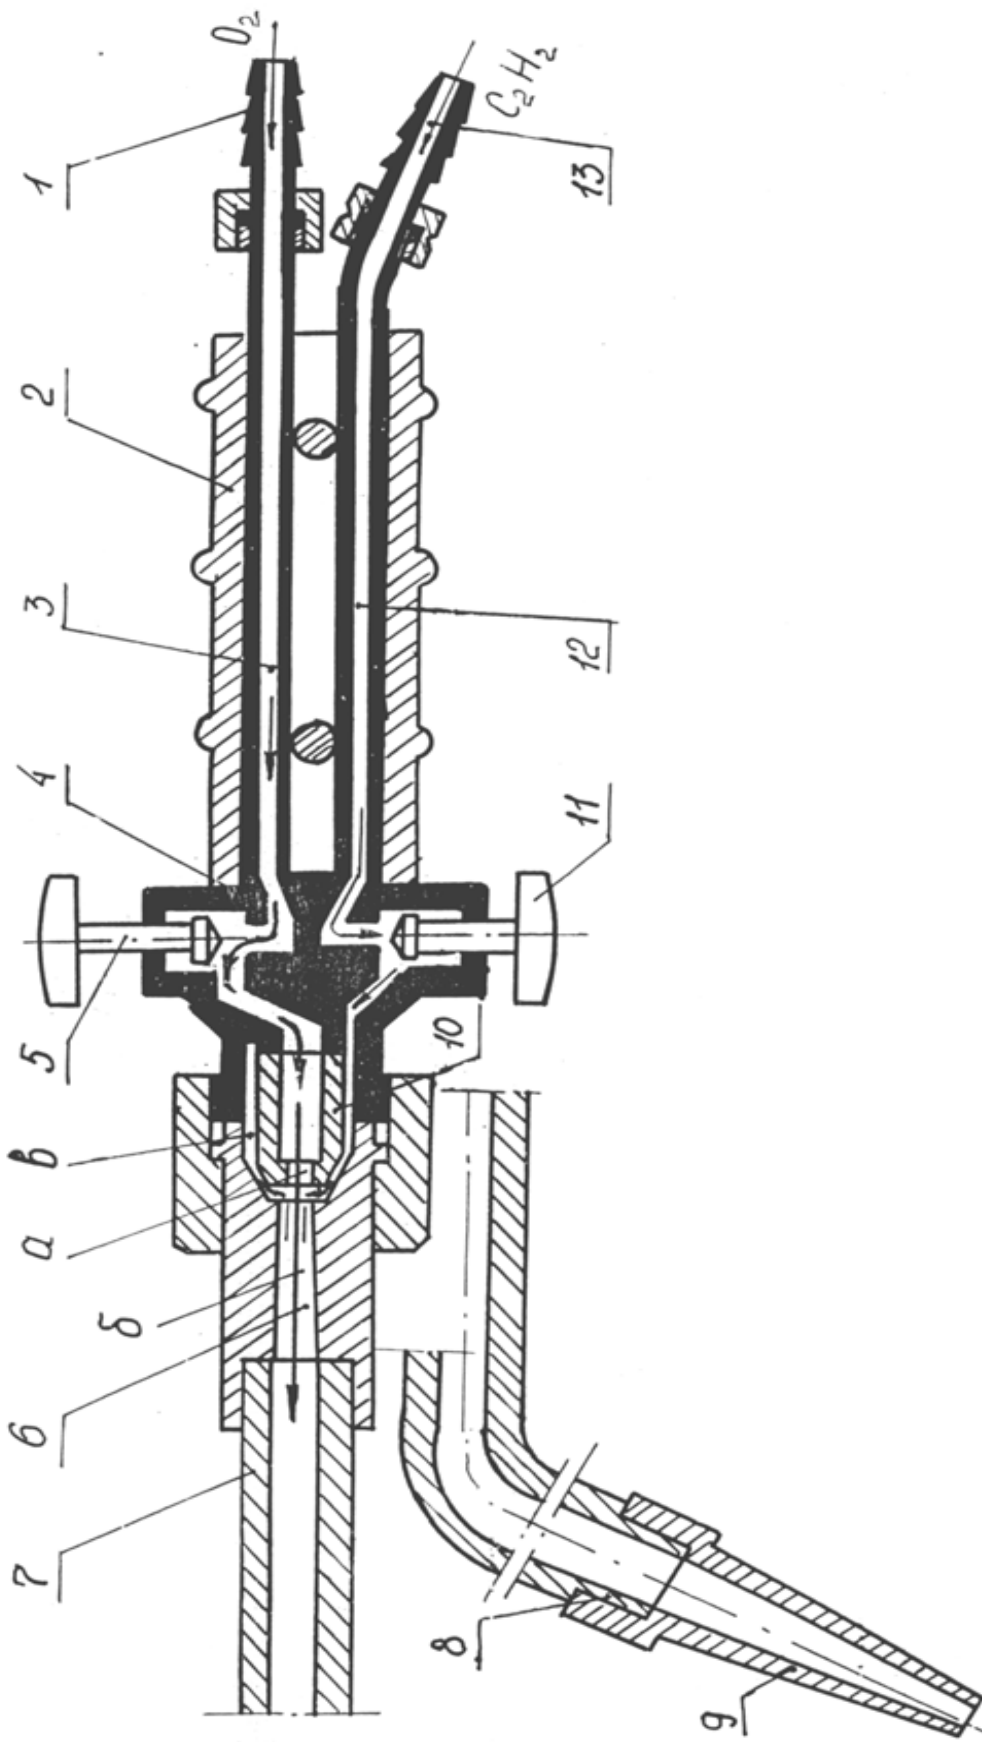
Схема инжекторной горелки. 1 - кислородный нипель; 2 - рукоятка горелки; 3 - трубка для транспортирования кислорода; 4 - корпус; 5 - вентиль кислорода; 6 - смешительная камера; 7 - трубка для подачи горючей смеси; 8 - штуцер; 9 - мундштук; 10 - инжектор; 11 - вентиль ацетилена; 12 - трубка для транспортирования ацетилена; 13 - ацетиленовый нипель; а - канал инжектора; б - канал смешительной камеры; в - зазор инжектора ацетилена
